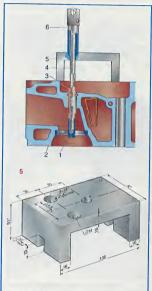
Выпрессовка направляющей втулки клапана двигателя "Волги" ГАЗ-24: 1 – наконечник; 2 – головка блока цилиндров; 3 – втулка клапана; 4 – шпилька; 5 – опора; 6 – гайка.
